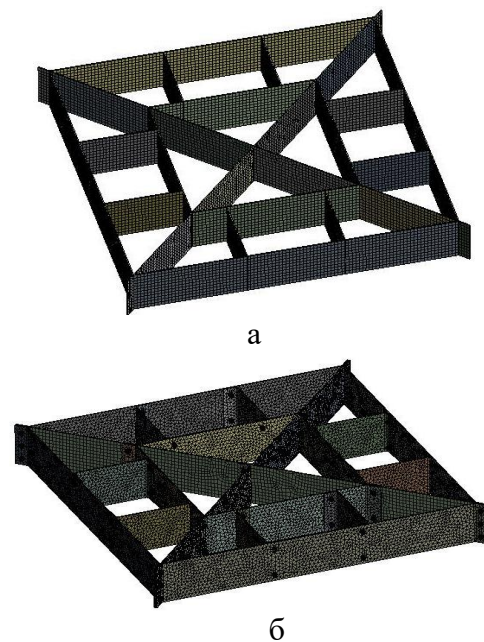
Конечно-элементные модели металлоконструкций грузовых тележек с универсальной компоновочной схемой: а – модель металлоконструкции со сварными соединениями; б – модель металлоконструкции с болтовыми соединениями
